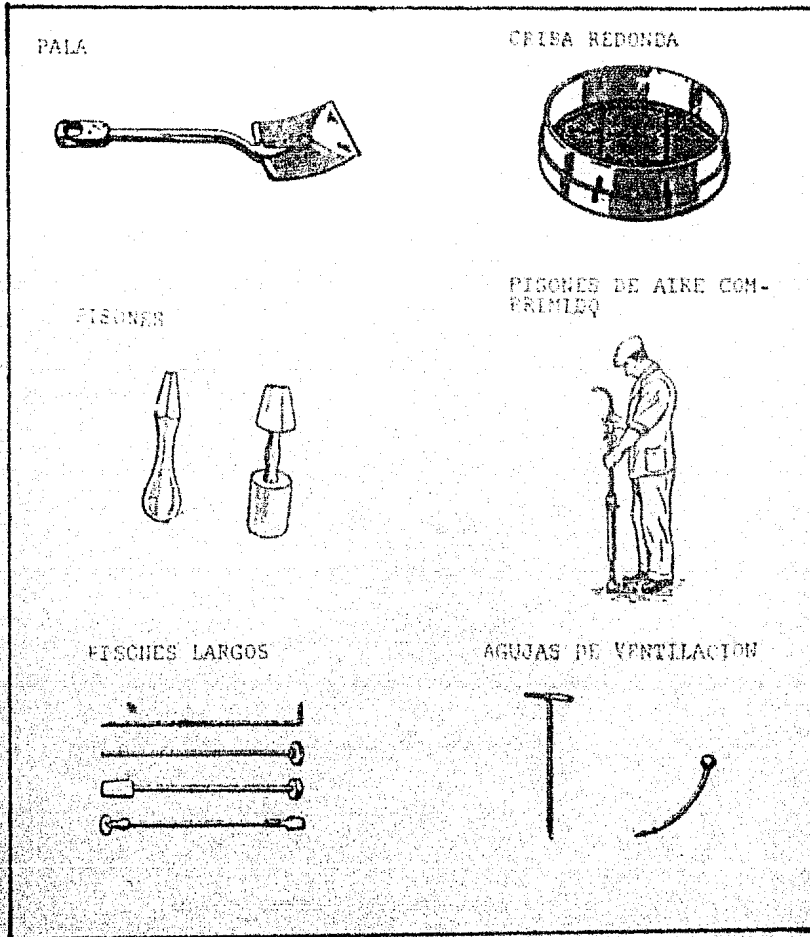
UTILES DE MOLDEO PARA LLENAR LAS CAJAS DE MOLDEO.
